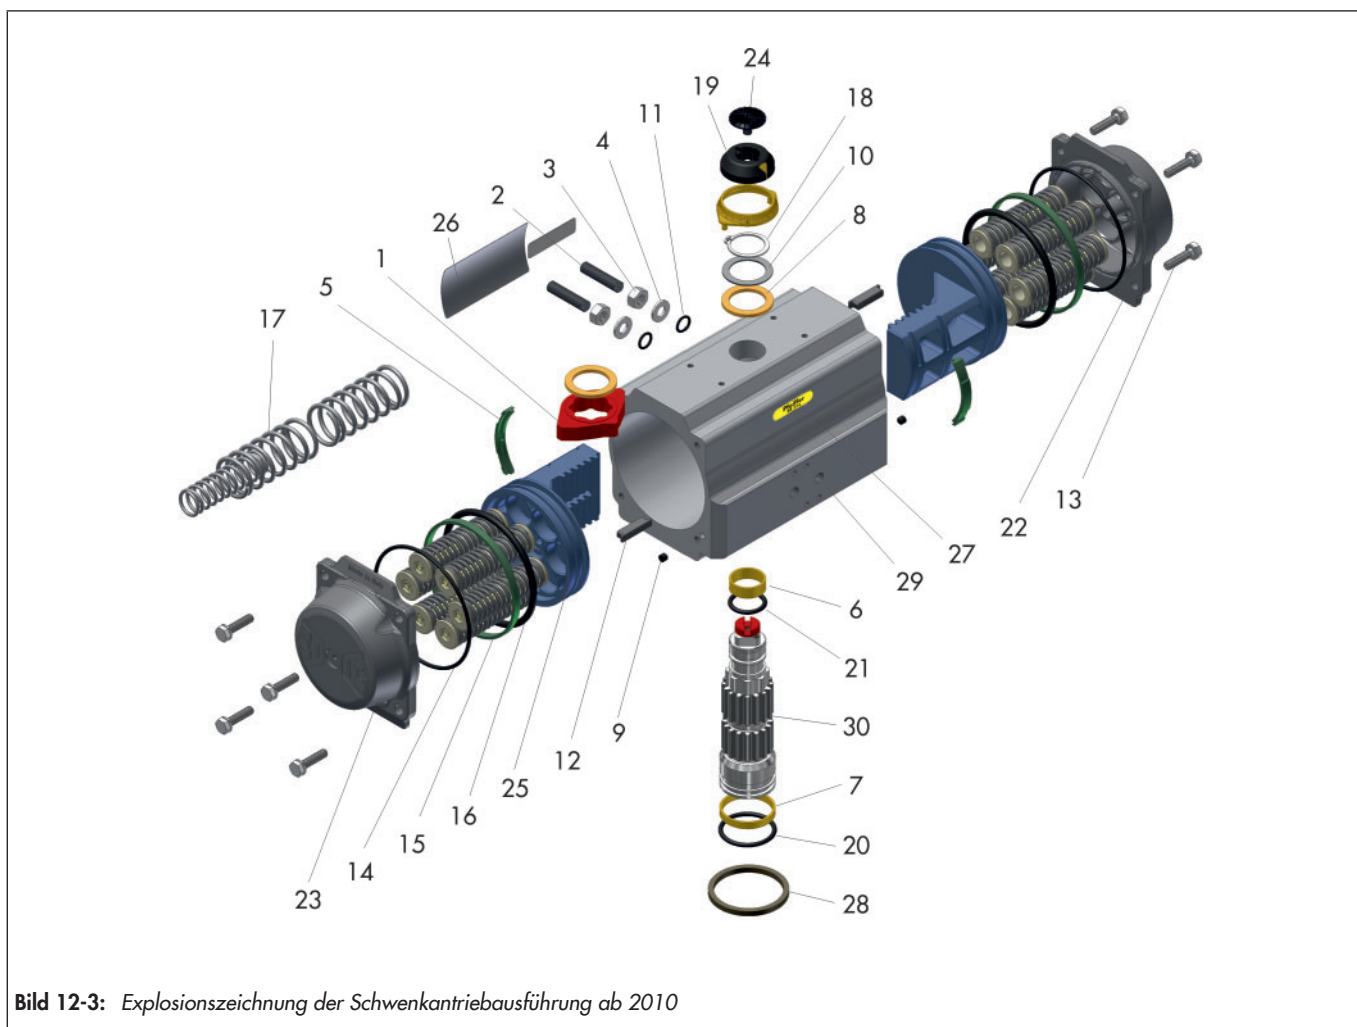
Explosionszeichnung der Schwenkantriebsausführung ab 2010
